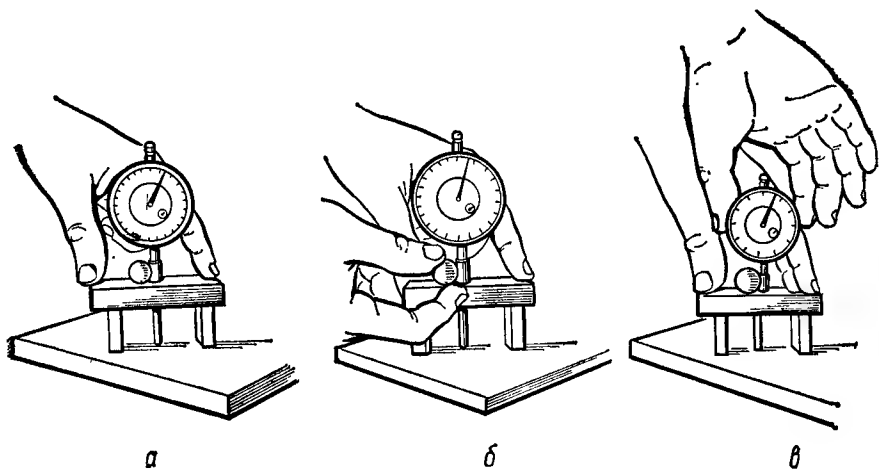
Установка индикаторного глубиномера в нулевое положение.
